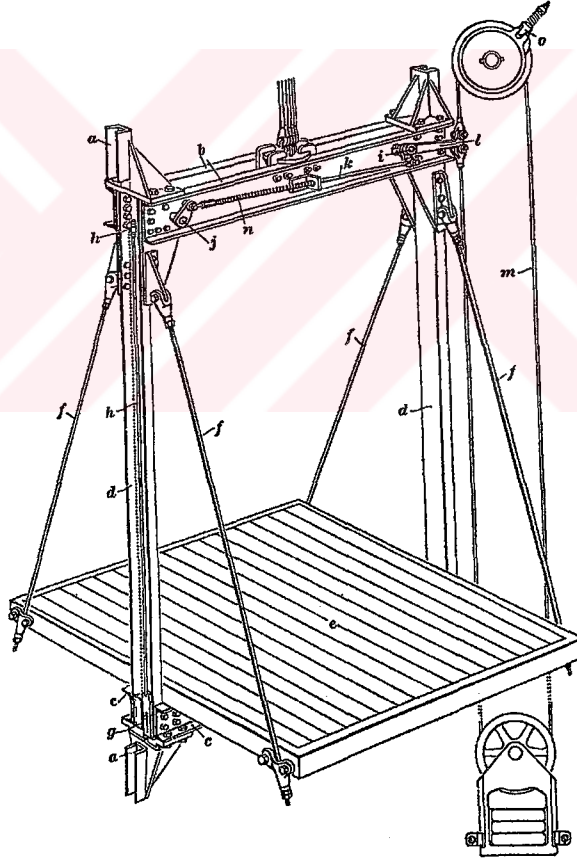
Asansör kabin çerçevesi montajı [9].
